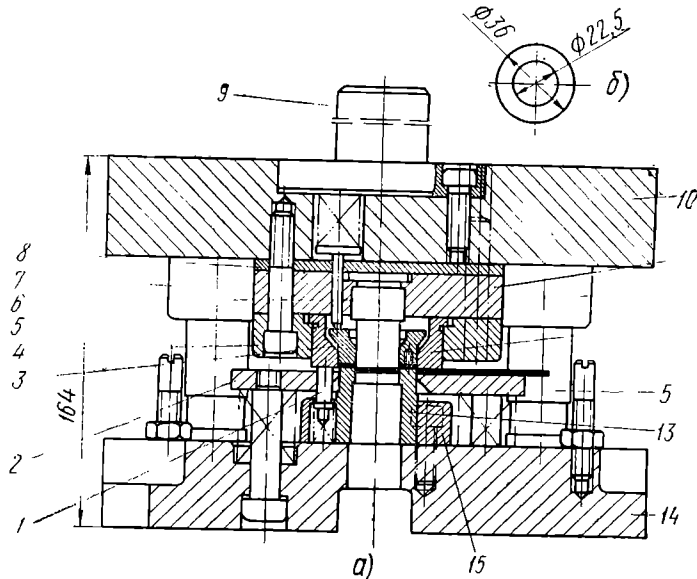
Комбинированный штамп для совмещенных пробивки отверстия и вырубки (а) шайбы из стали 08 т. толщиной 0,5 мм (б)
